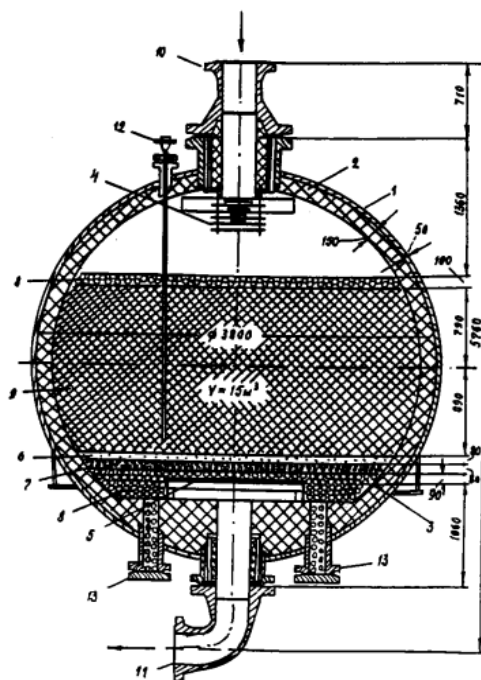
Сферический реактор с аксиальным направлением потока [28]:
